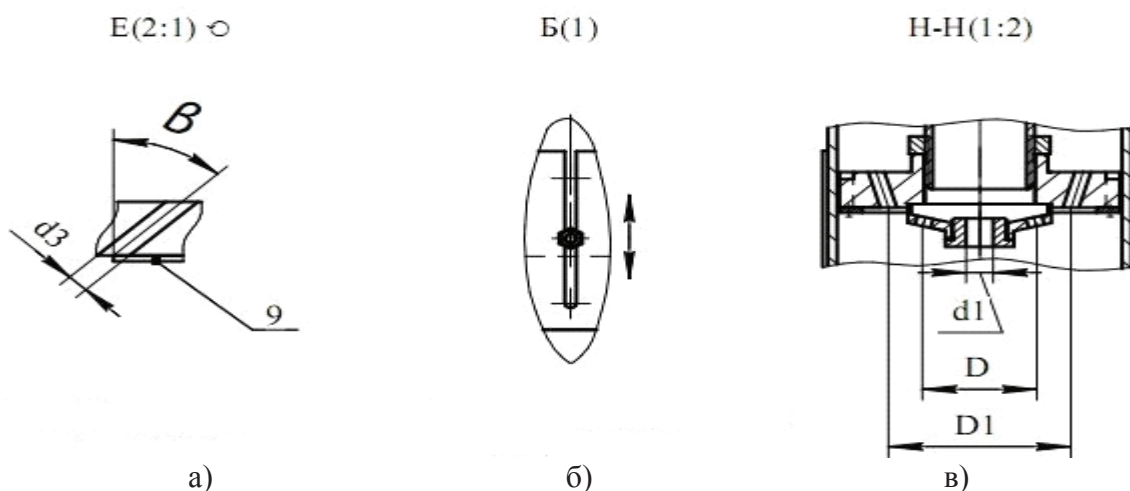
Дополнительные виды на горелку: а) вид на воздушные отверстия; б) крепление конуса к корпусу; в) поперечный разрез насадки
